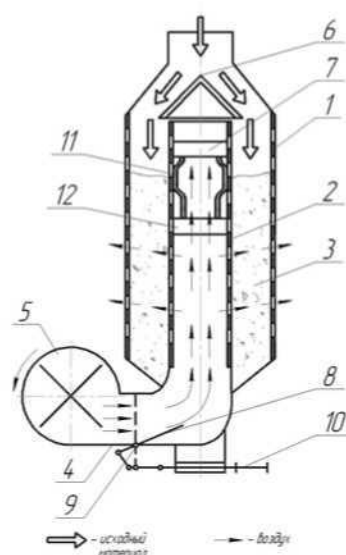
Предложенный бункер с самоустанавливающимся клапаном:
